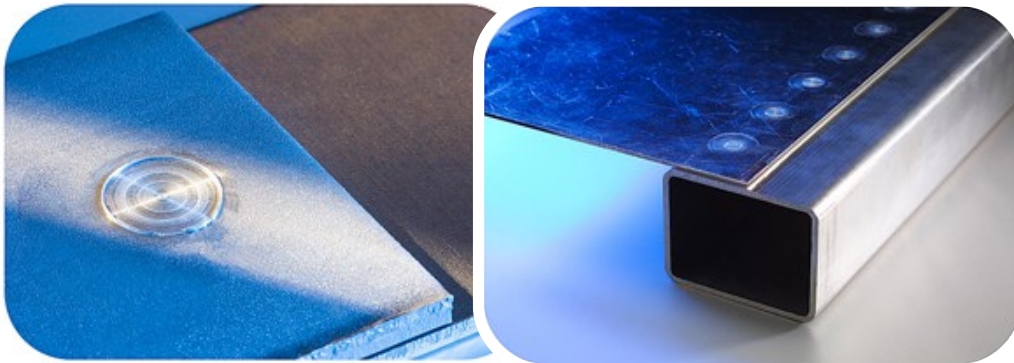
exemples de pièces soudées (source: Riftec GmbH)
